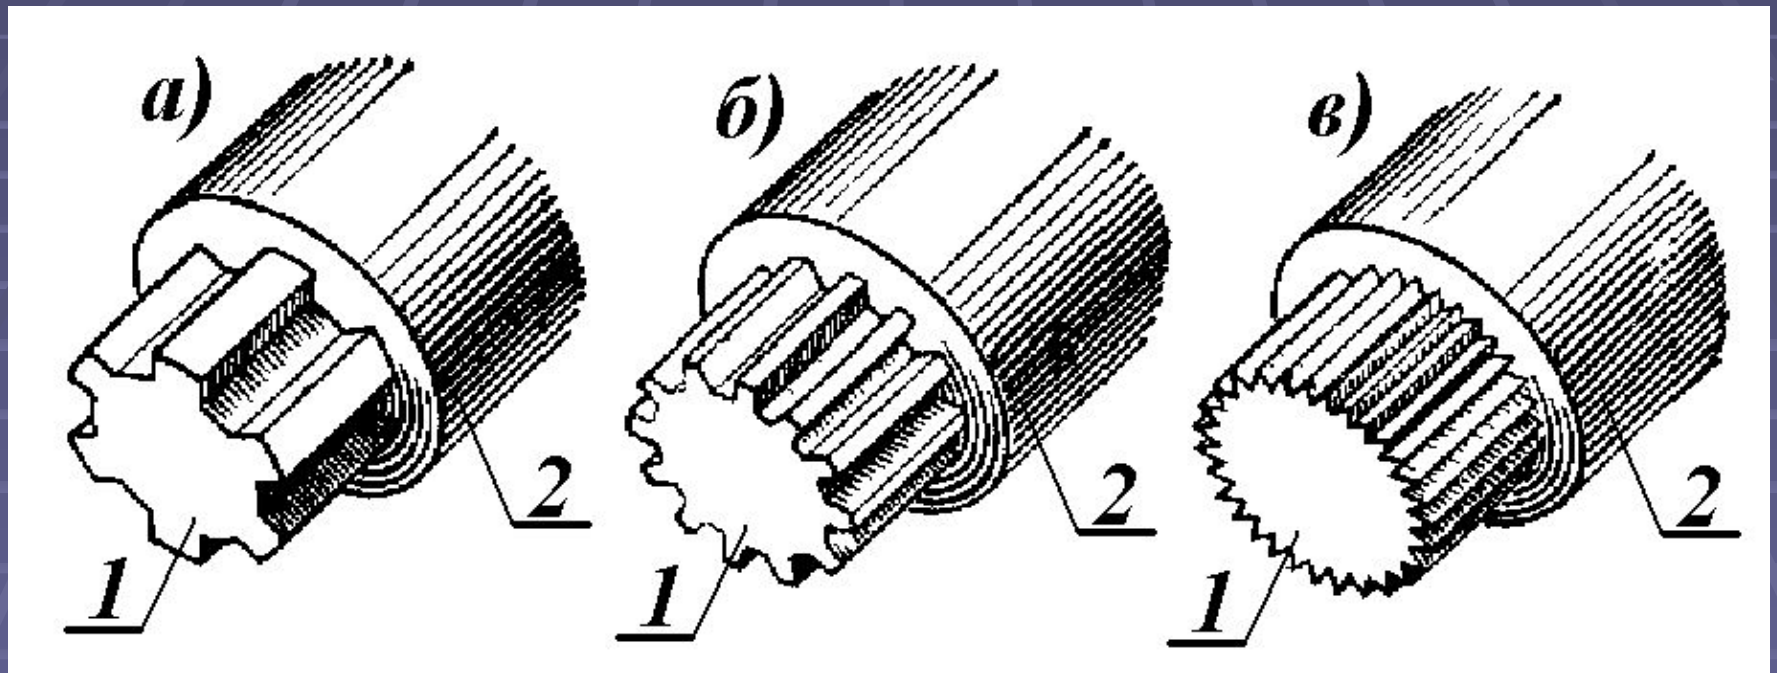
Шлицевое соединение: а) прямобочными шлицами; б) эвольвентными шлицами; в) треугольными шлицами; 1 – вал, 2 – ступица.
